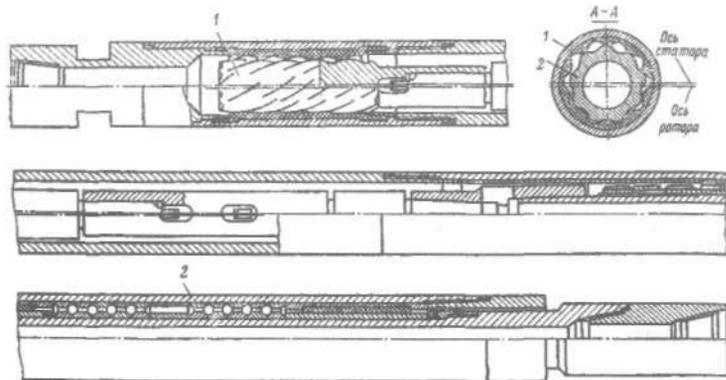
Винтовой забойный двигатель Д - 85:
